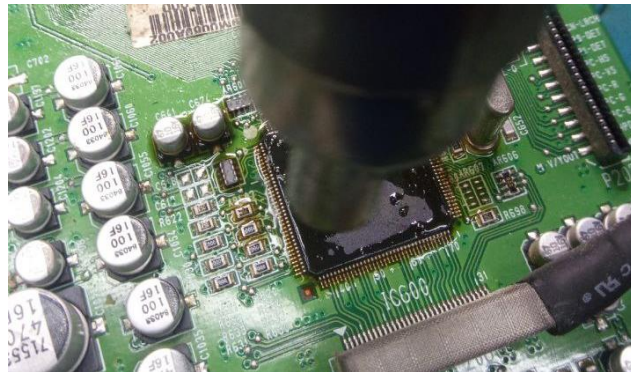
Desoldado de Integrado de montaje superficial de gran tamaño – Autoría propia
